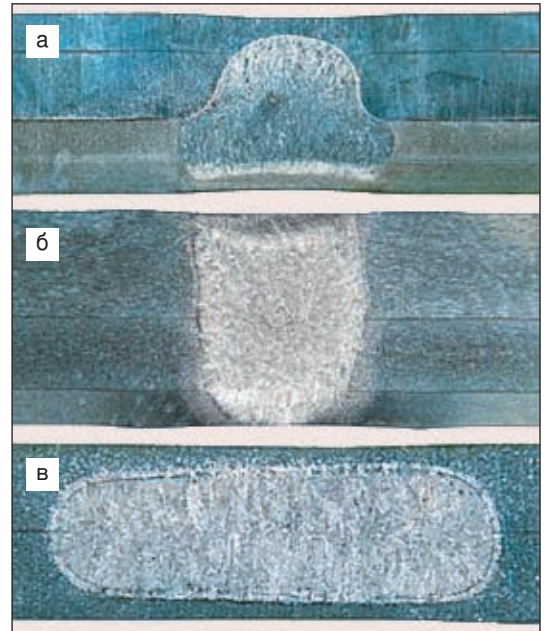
Макрошлифы поперечных сечений сварных соединений: а — трех листов из различных сталей разной толщины (1,8 мм+1,75 мм+1,0 мм), режим сварки: 8 кА, 500 мс, 4 кН; б — трех листов из алюминиевого сплава AlMg3 (3,0 мм+2,0 мм+1,0 мм), режим сварки: 17 кА, 700 мс, 4 кН; в — двух листов из электрогальванизированной стали DCO1 (1 мм+1 мм), режим сварки: 6,3 кА, 200 мс, 2,5 кН
